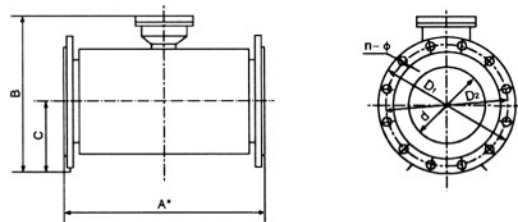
SHLDG-250S~1600S型传感器外形与安装尺寸
